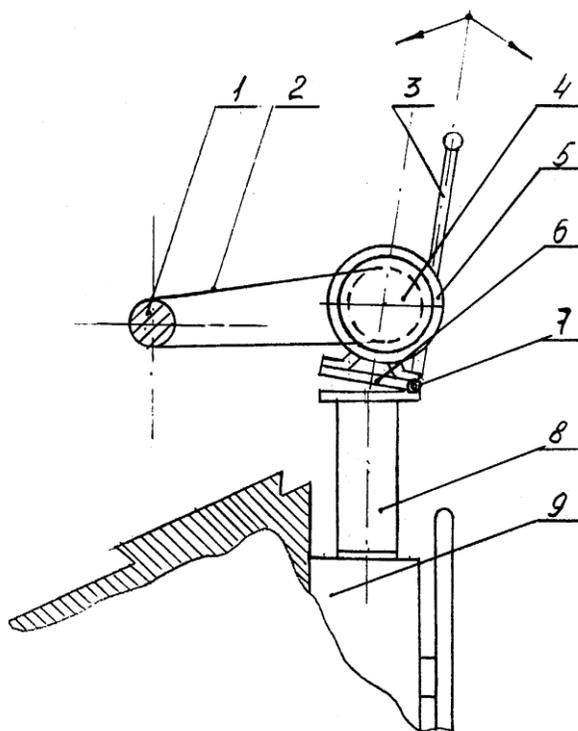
Ленточно-шлифовальное приспособление
